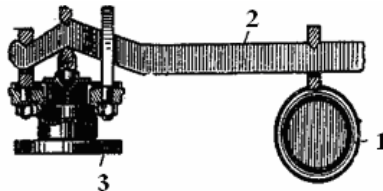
важільний запобіжний клапан: 1 - противага; 2 - важіль; 3 - корпус клапана
